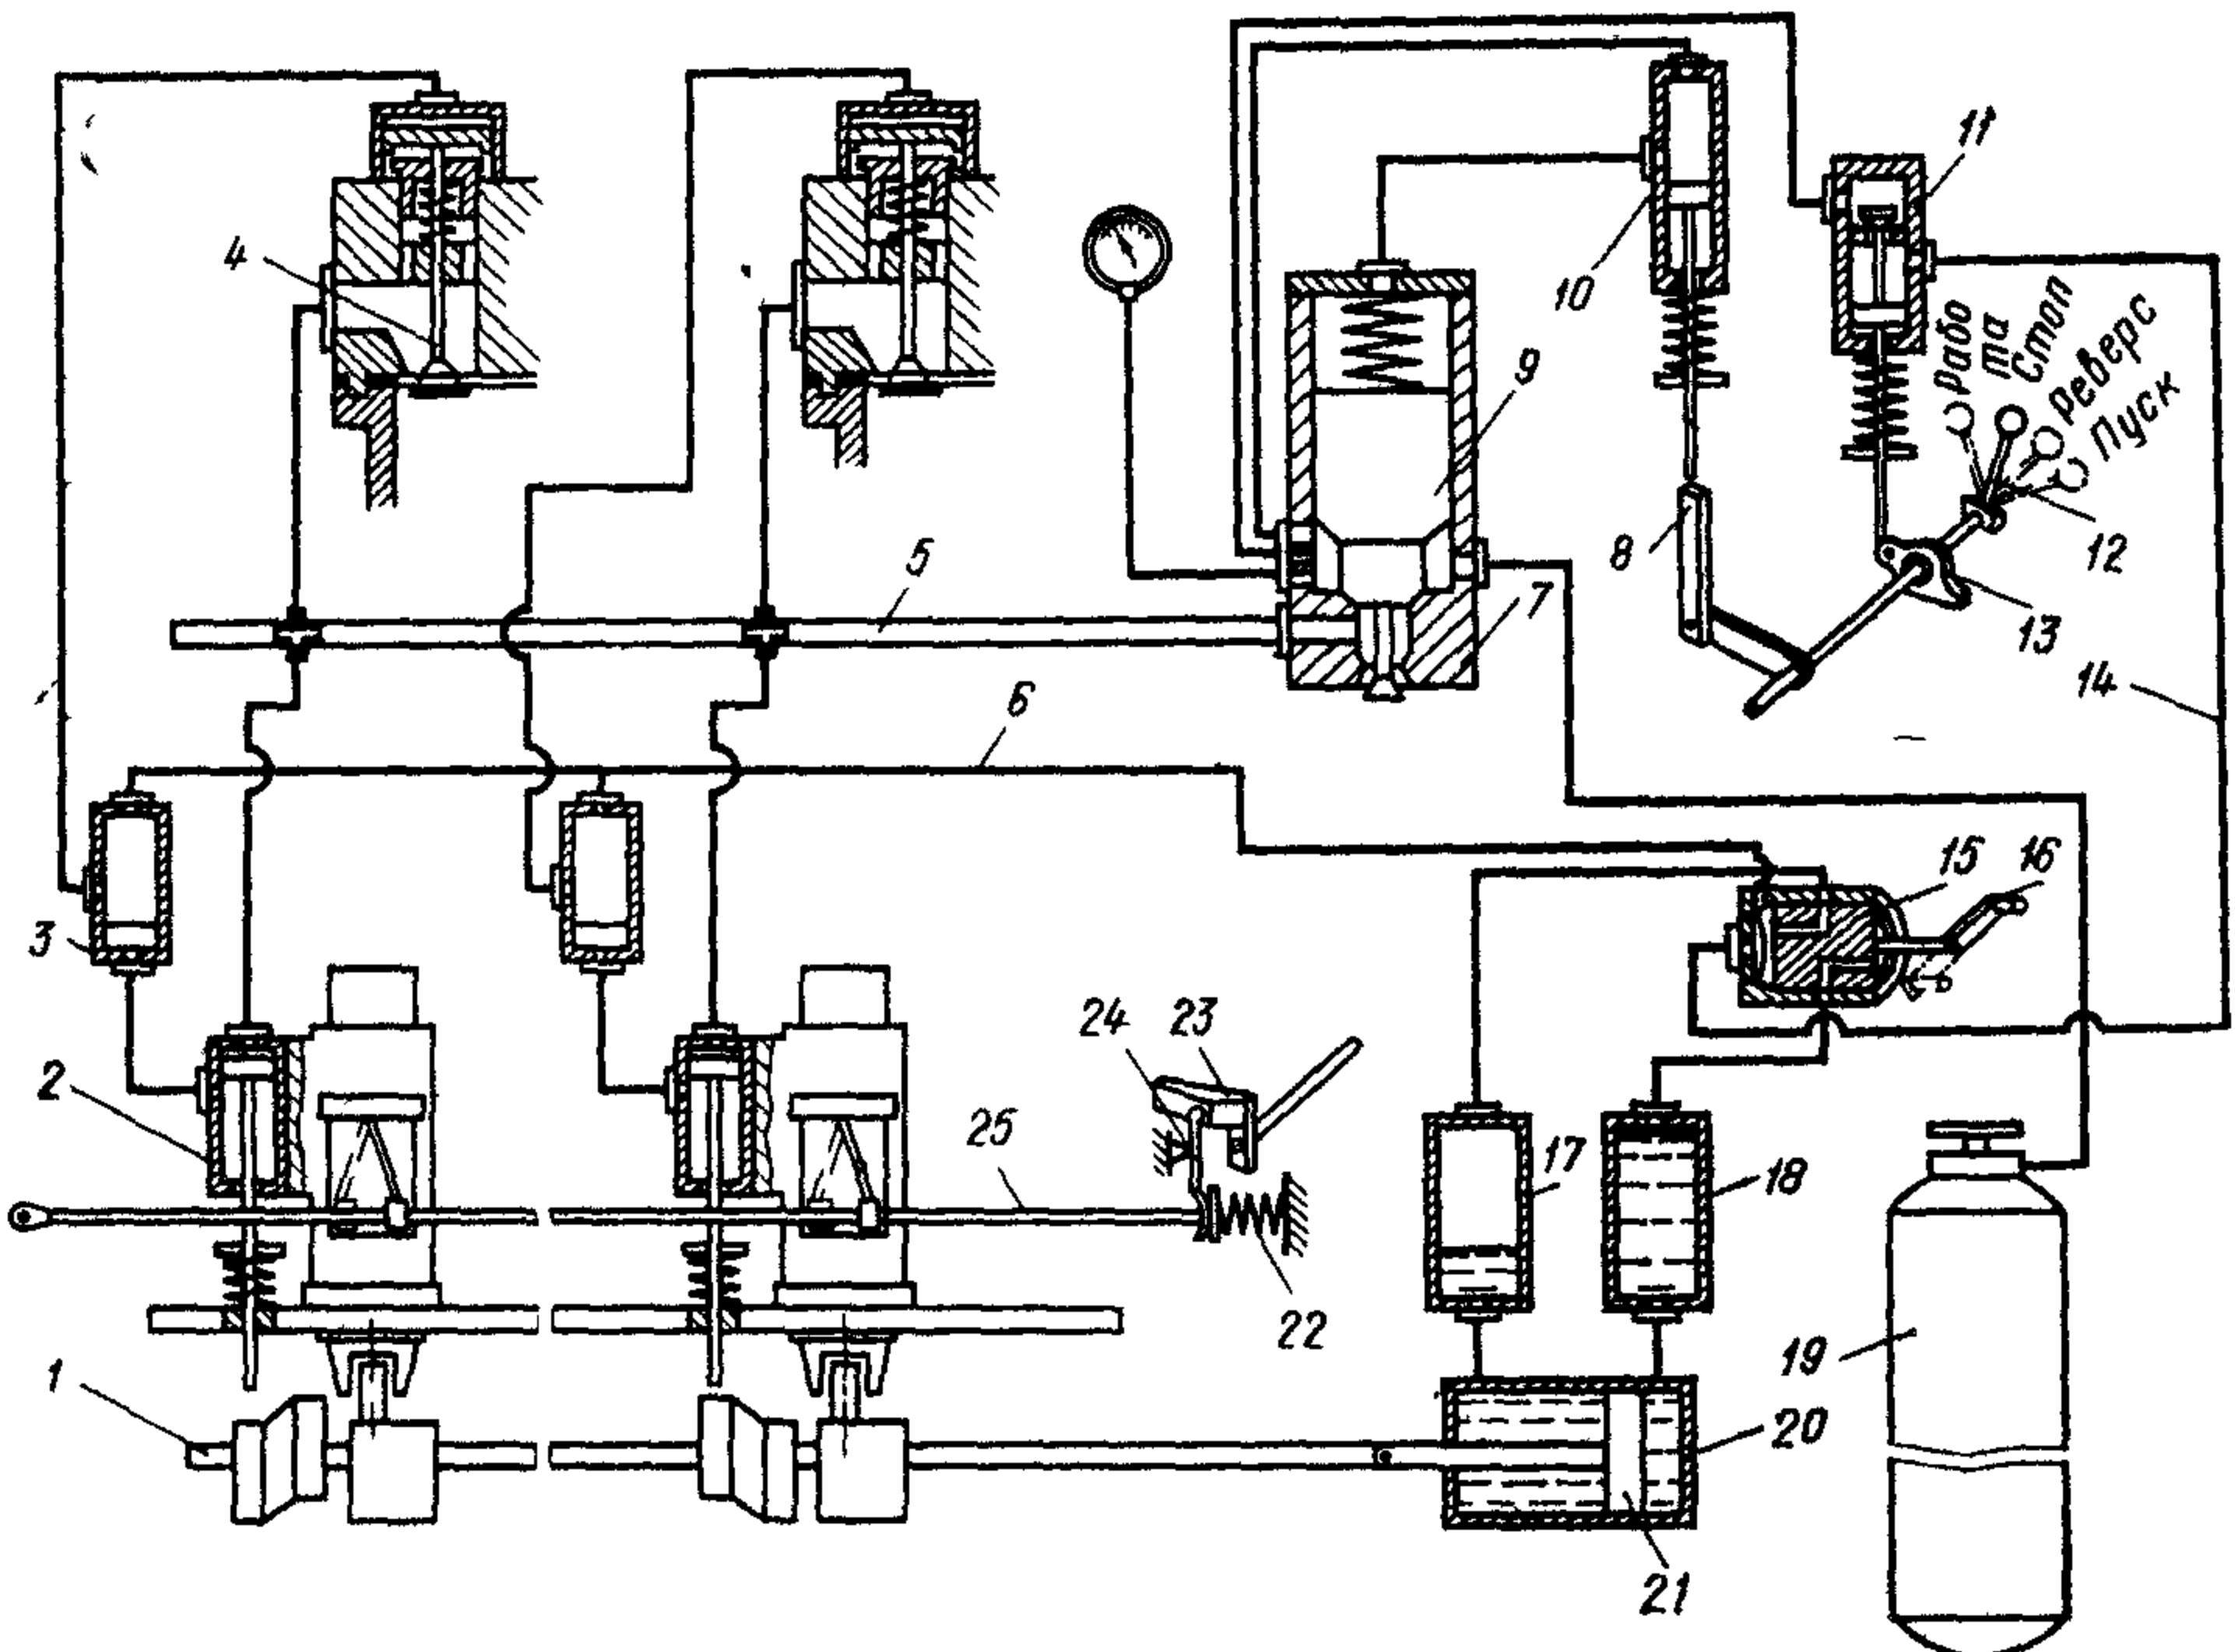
Схема реверсивного устройства двигателя типа НФД48У
